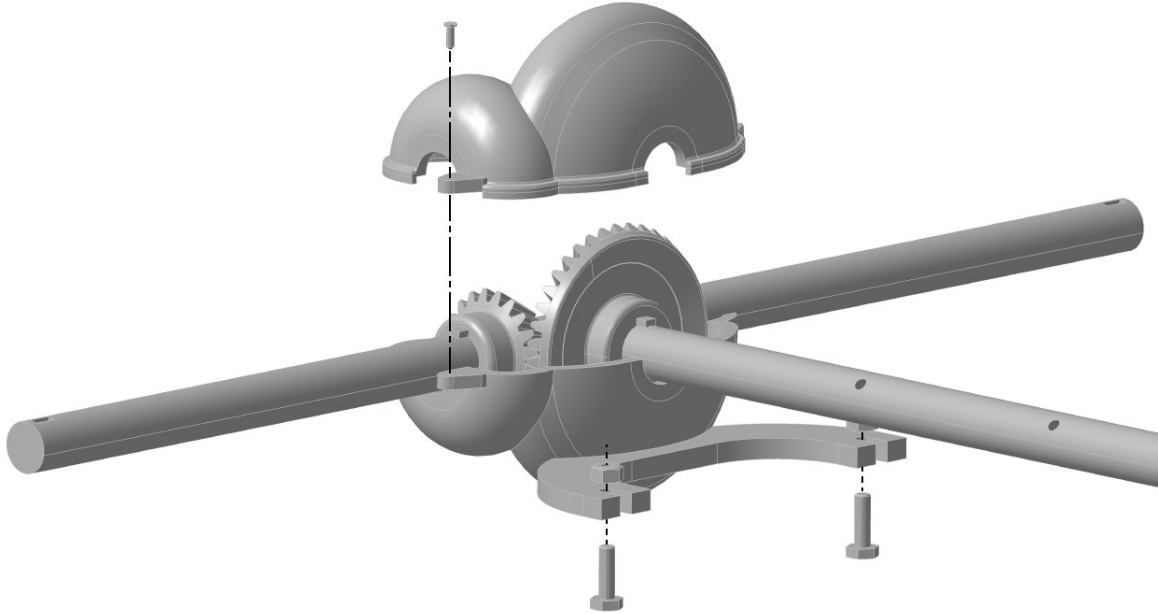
Vista explosionada de la carcasa del engranaje cónico.
